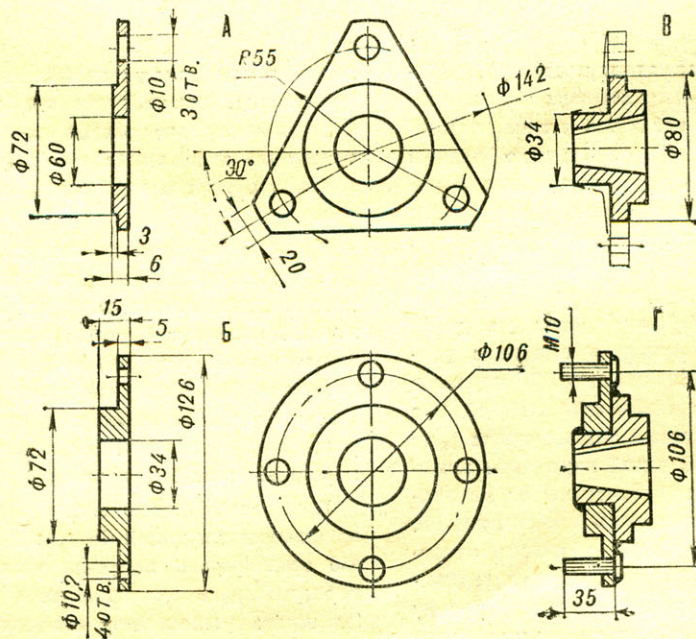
Детали для доработки заднего моста: А — переходный фланец крышки тормозного барабана СЗД; Б — переходный фланец ступицы заднего колеса (под тормозной барабан мотоколяски СЗД); В — доработка ступицы СЗД; Г — фланец и ступица в сборе.
